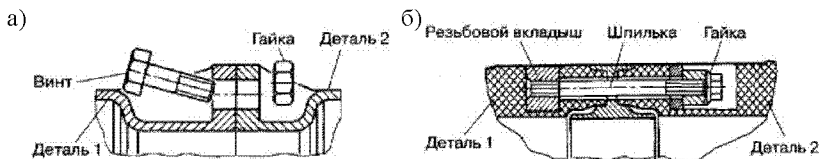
Конструктивные приемы обеспечения сборки
